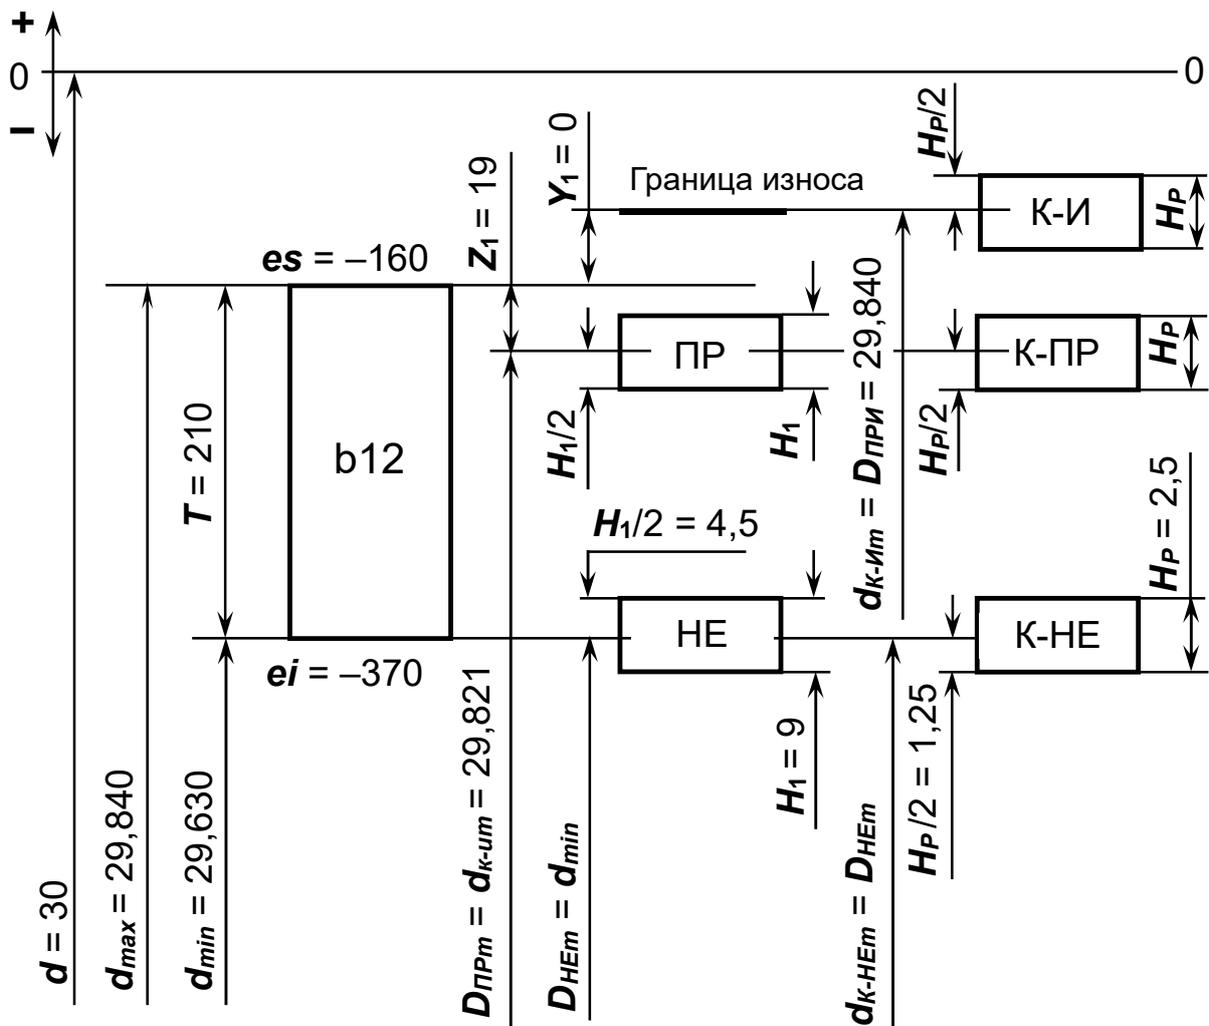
Схема расположения полей допусков рабочих калибров-скоб для проверки деталей валов размером $\text{Ø}30b12$ и полей допусков контрольных калибров для проверки рабочих калибров-скоб
